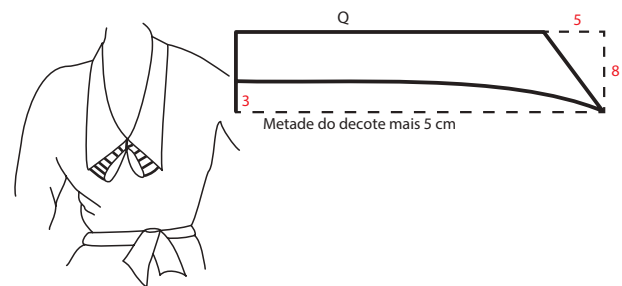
Desenho e molde para variante de gola pontiaguda.
